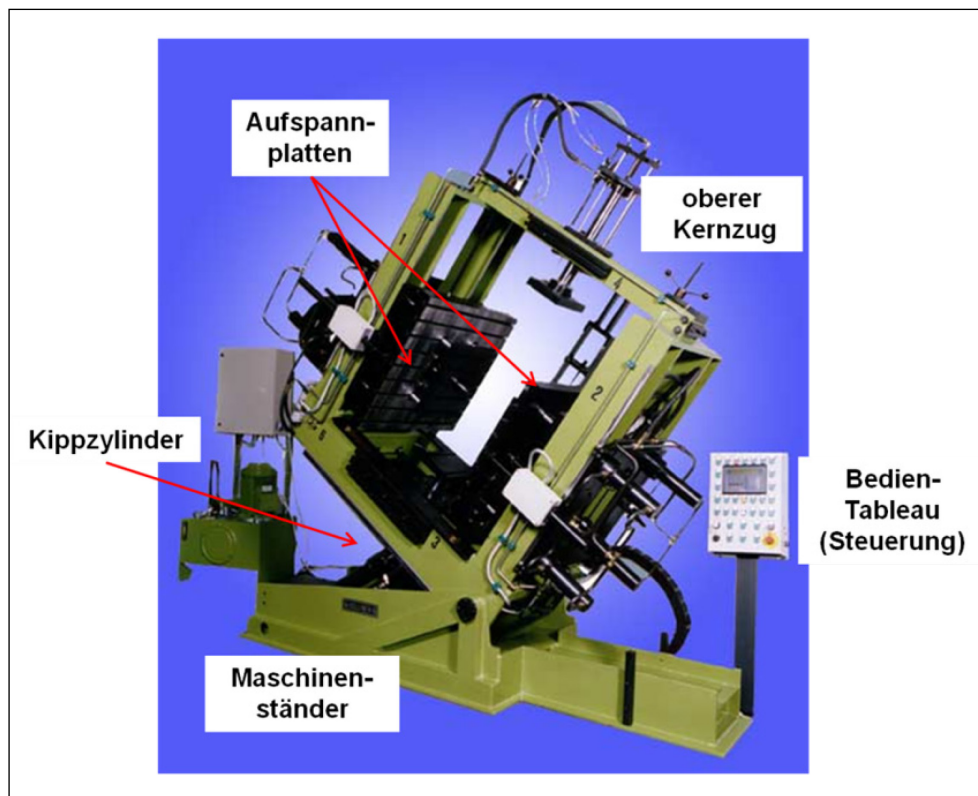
, Kippgießmaschine für das Kokillengießverfahren (Quelle: Göllner Maschinenbau GmbH, Paderborn)
